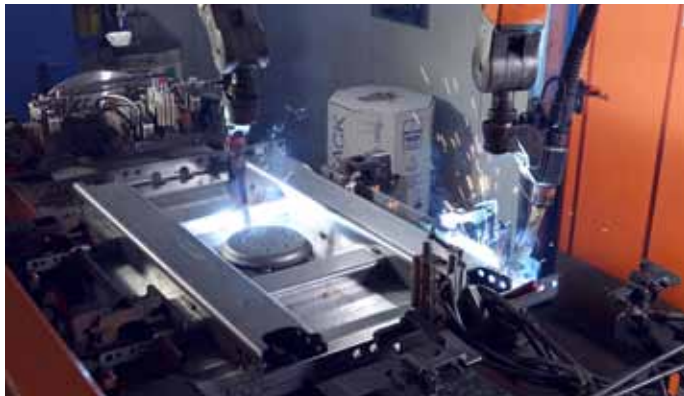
CLOOS-Roboter schweißen Bauteile für LKW-Auflieger.
